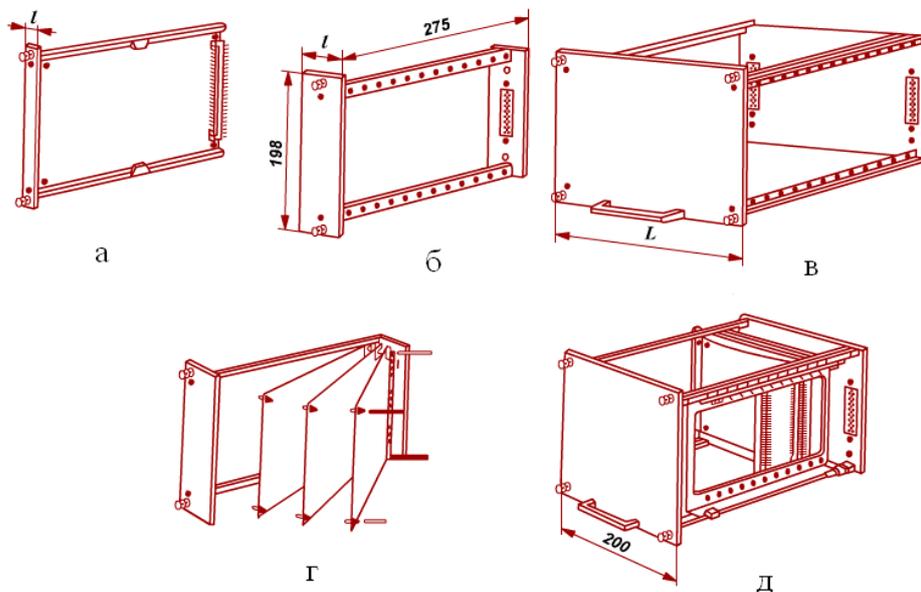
Схема конструкций частичных корпусов: а – для размещения одной платы; б – для размещения двух плат, в - для крупногабаритных ЭРЭ и источников питания; г – для «книжной компоновки»; д – для «разъемной» компоновки (платы вставляются сбоку)
